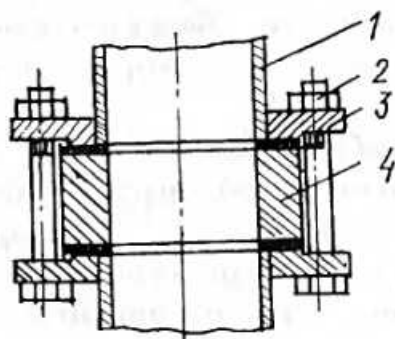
Встановлення монтажної шайби замість вимірювальної діафрагми: 1 - патрубок; 2 - болт з гайкою; 3 - фланець; 4 - шайба
